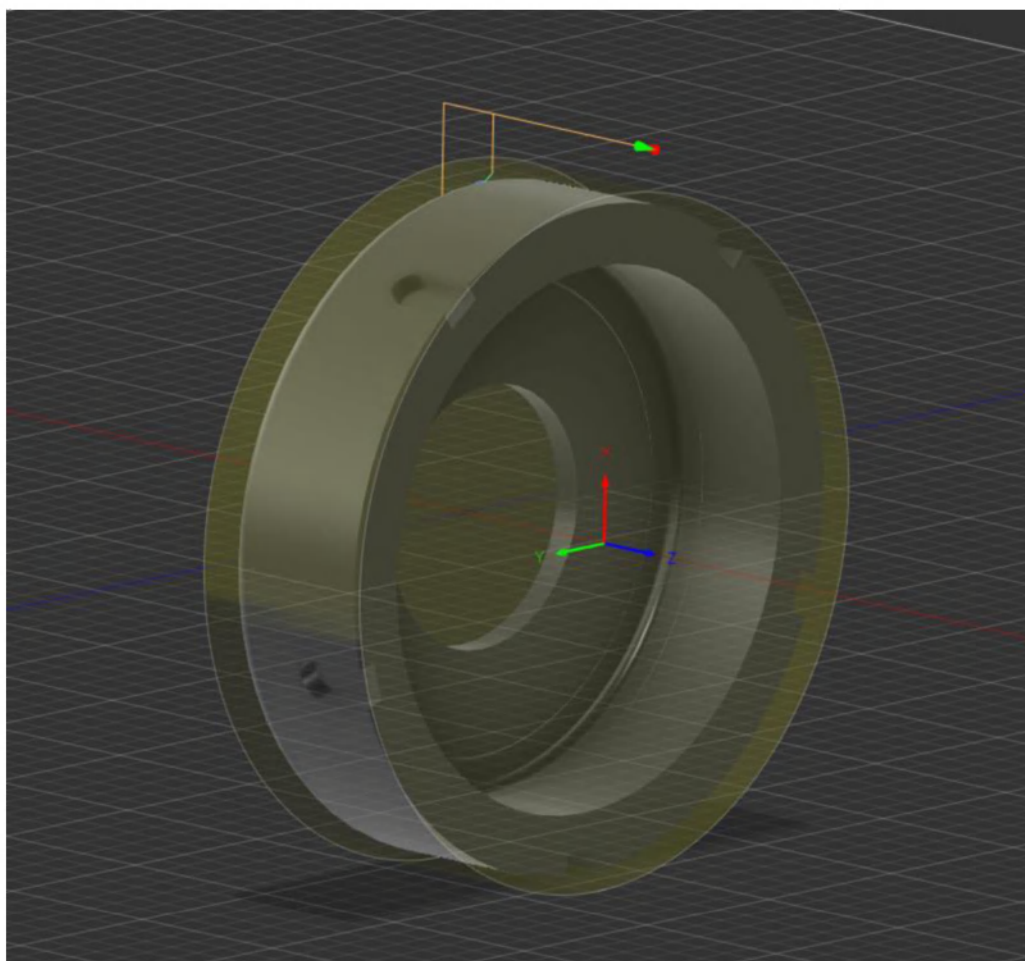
Передня зовнішня кришка (сірий колір) та заготовка (жовтий) з якої буде виготовлятися деталь
